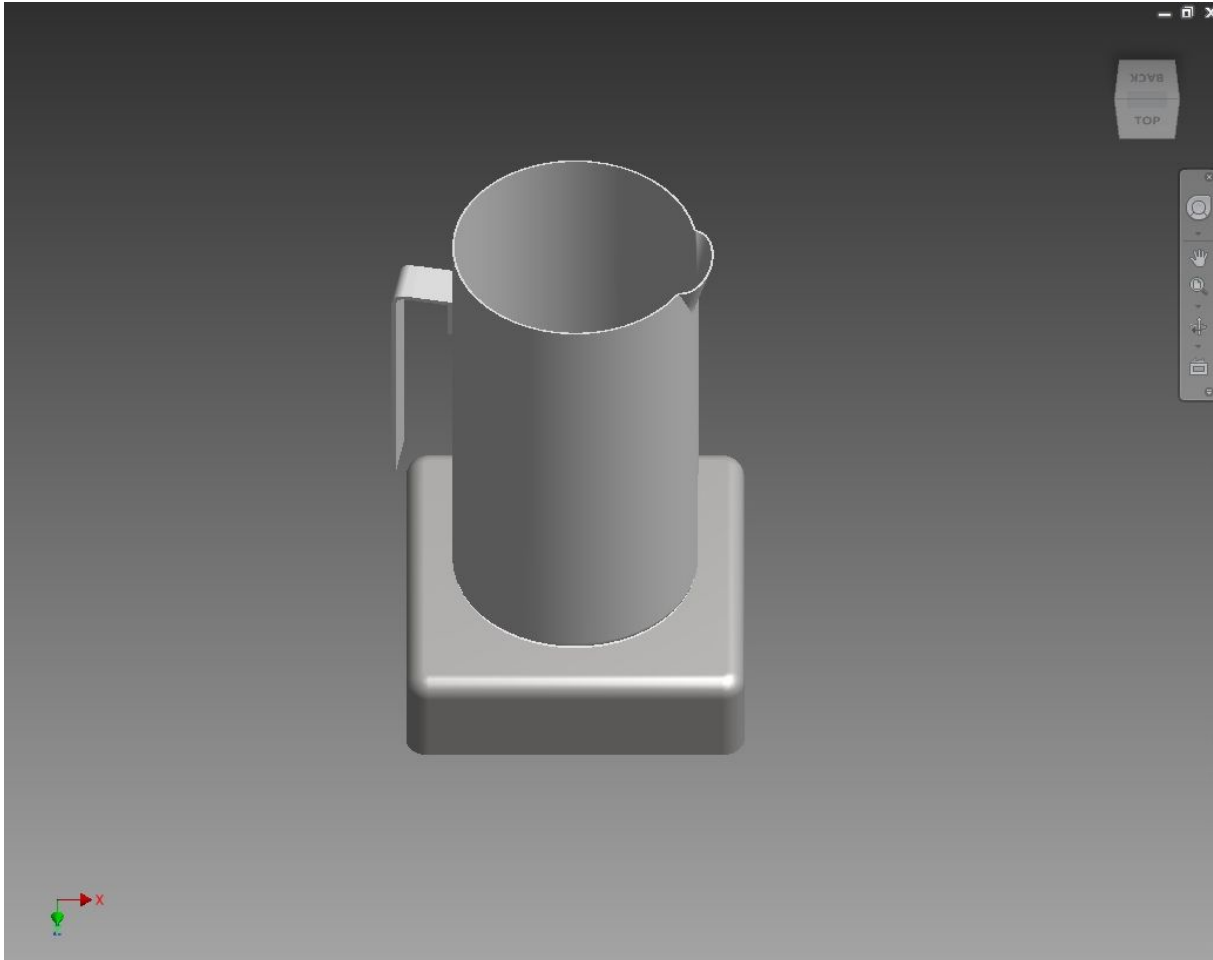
Ensamble de partes y máquina terminada en 3D en el programa Inventor
